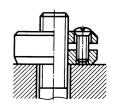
Способы стопорения дополнительной резьбовой деталью
